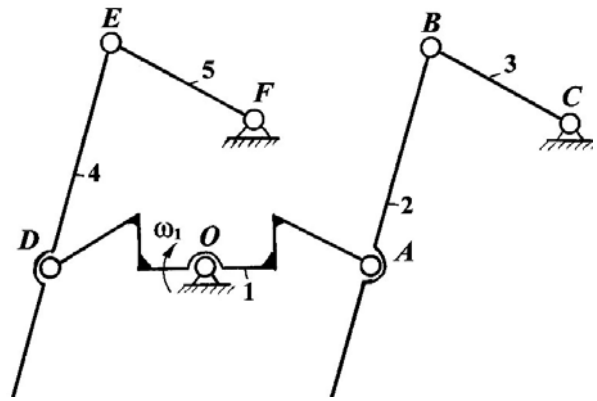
Механизм привода упаковщика пресс-подборщика
